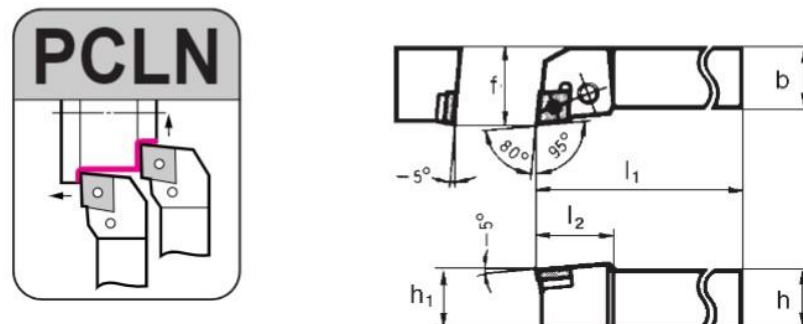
Державка PCLN R 2525 M12 [1, с. 122]
